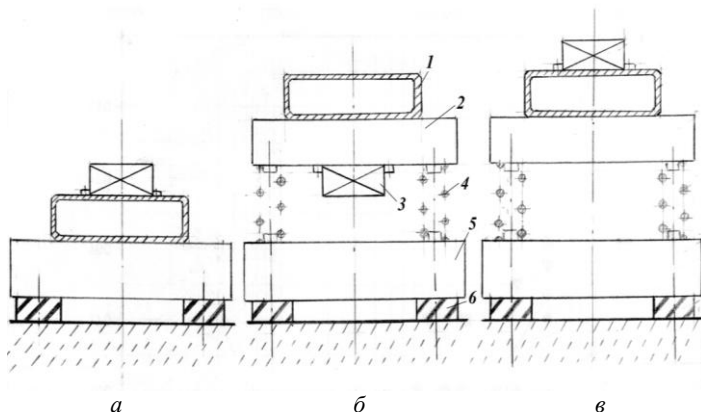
Схема расположения детали и вибратора: 1 – обрабатываемый корпус; 2 – верхняя плита вибростола; 3 – вибратор; 4 – пружина; 5 – нижняя фундаментная плита; 6 – виброизолирующие прокладки
